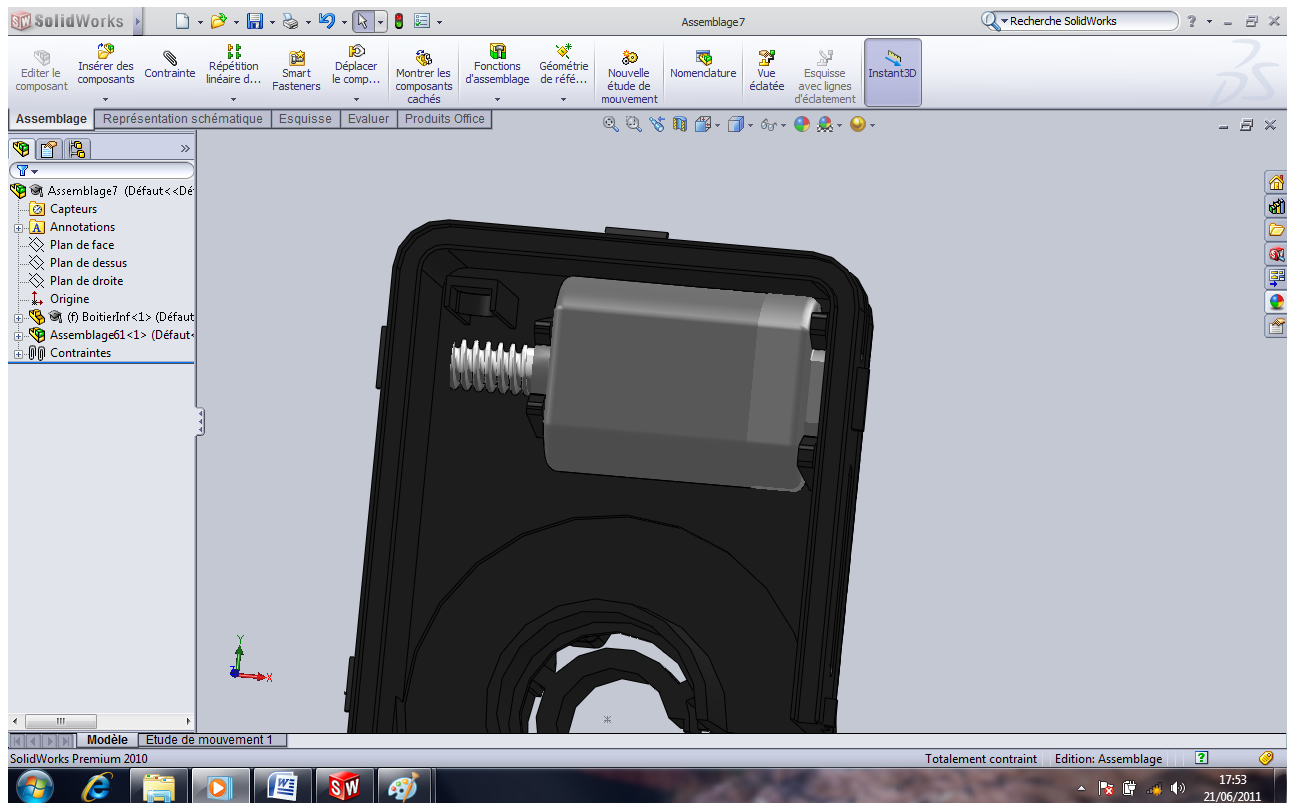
Assemblage 7(assemblage 6+boitier inferieur)
